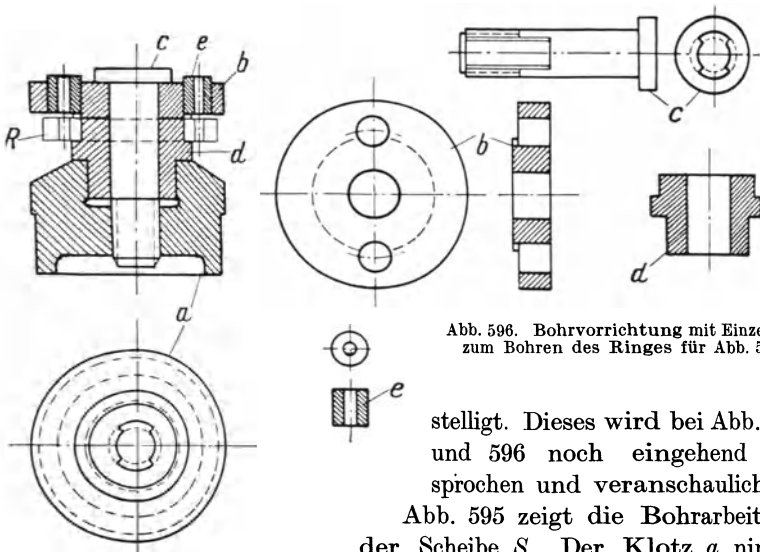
Bohrvorrichtung mit Einzelteile zum Bohren des Ringes für Abb. 588.
